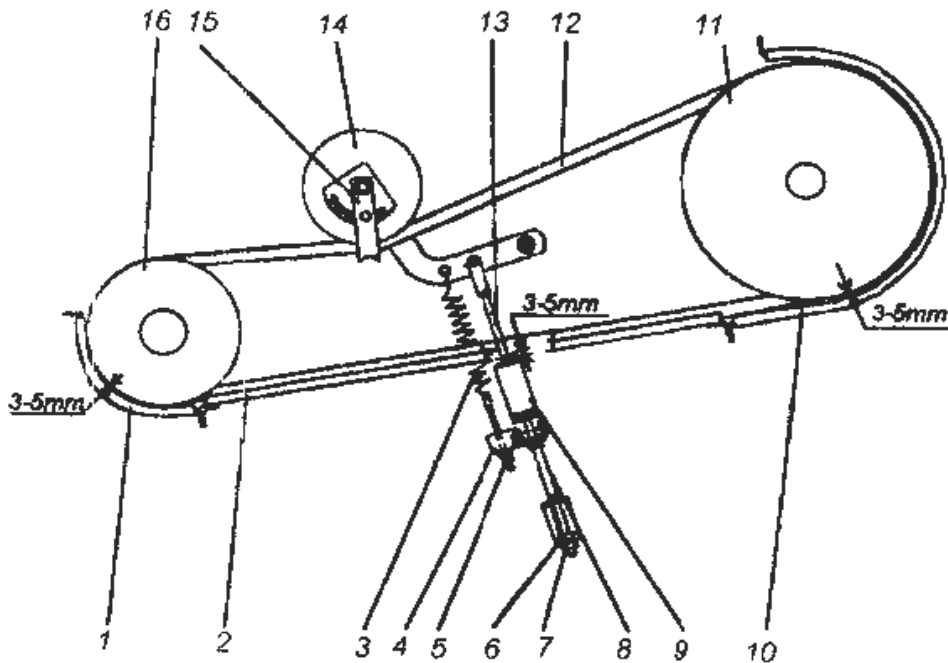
Механизм управления приводом жатвенной части: 1, 10 – кожухи; 2 – успокоитель; 3 – пружина; 4, 5, 6, 7 – гайки; 8 – устройство натяжное; 9 – гидроцилиндр; 11, 16 – шкивы; 12 – ремень; 13 – шток; 14 – шкив натяжной; 15 – кронштейн
